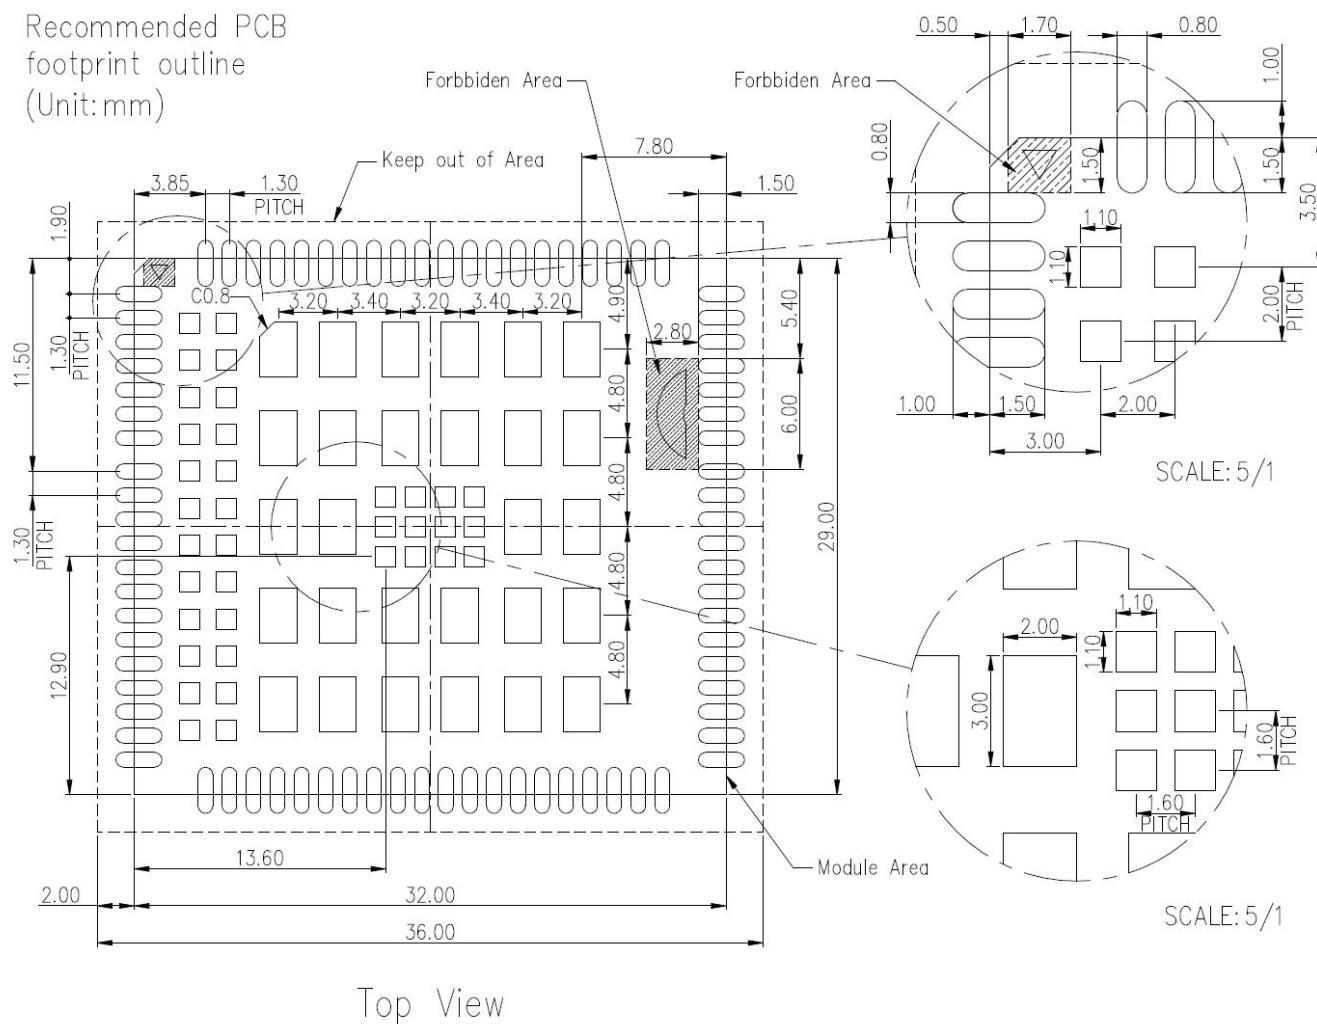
推荐 PCB 封装尺寸(单位: 毫米)
